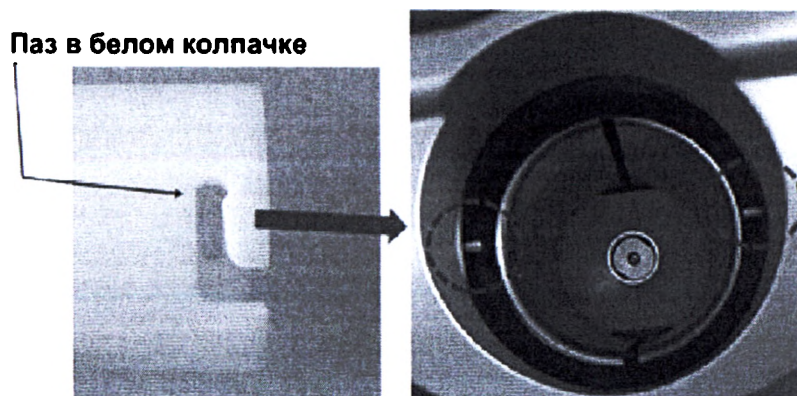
Проверка расположения пазов белого колпачка и пазов на корпусе изделия
